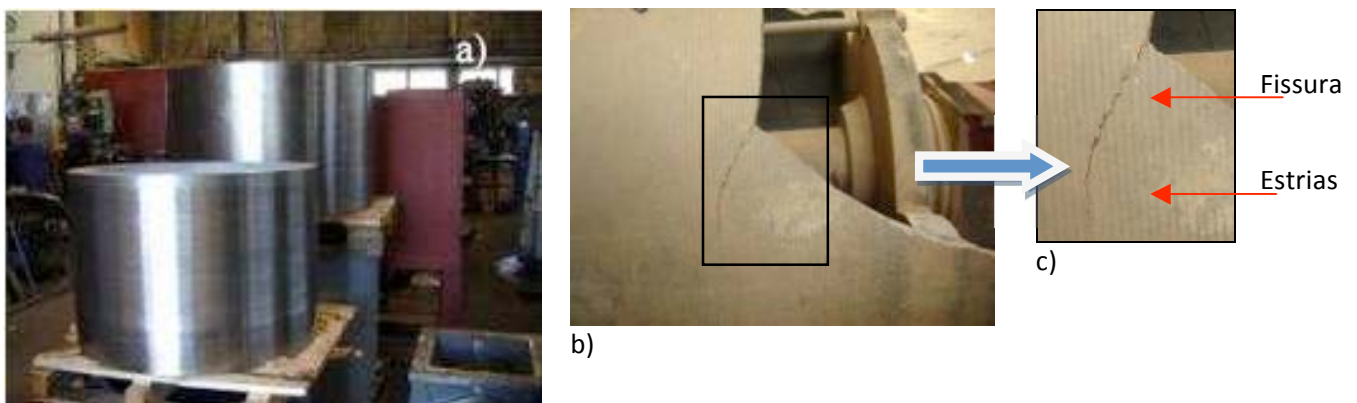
a) Rolos de laminagem produzidas pela CM&W após a maquinação; b) Rolo de laminagem partido, apresentando estrias preferencialmente num dos lados; c) pormenor da fissura e das estrias.
